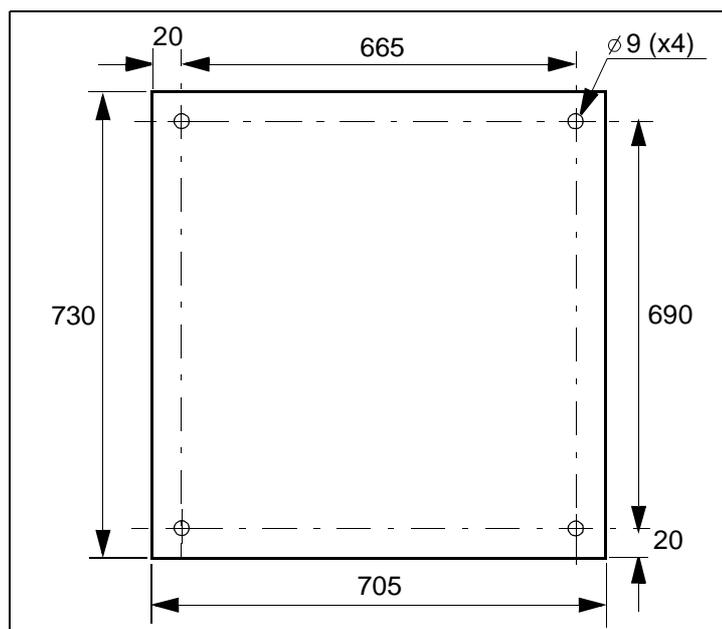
Placa de montaje para el montaje de equipo (dimensiones en mm)
